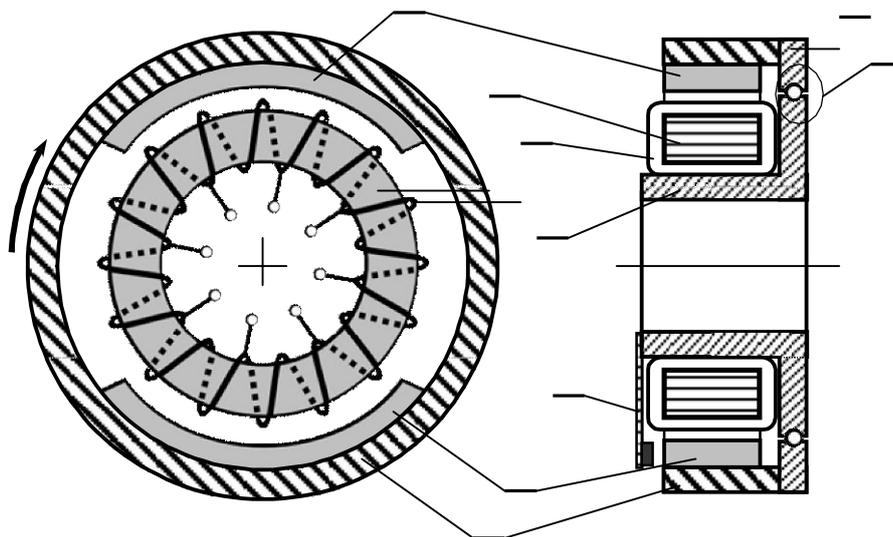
Вентильный двигатель постоянного тока (обращенной конструкции)
